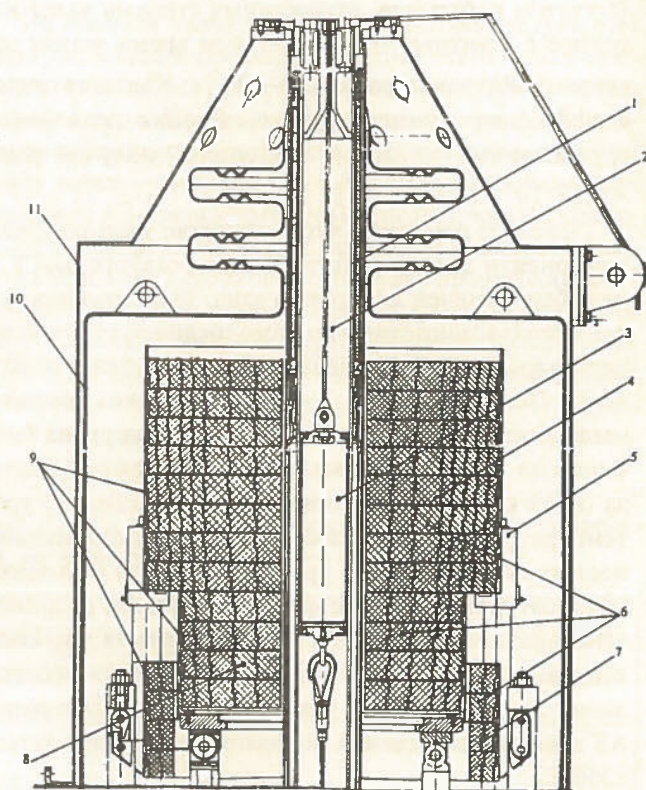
Конструкция АЗ реактора БИГР в осевом разрезе: 1 — импульсный блок; 2 — осевая полость; 3 — контейнер для облучения образцов; 4 — неподвижная часть АЗ; 5 — опора неподвижной части АЗ; 6 — уран-графитовые кольца; 7 — блок точного регулирования реактивности; 8 — блок грубого регулирования реактивности; 9 — опоры секций АЗ; 10 — корпус АЗ; 11 — кожух охлаждения
